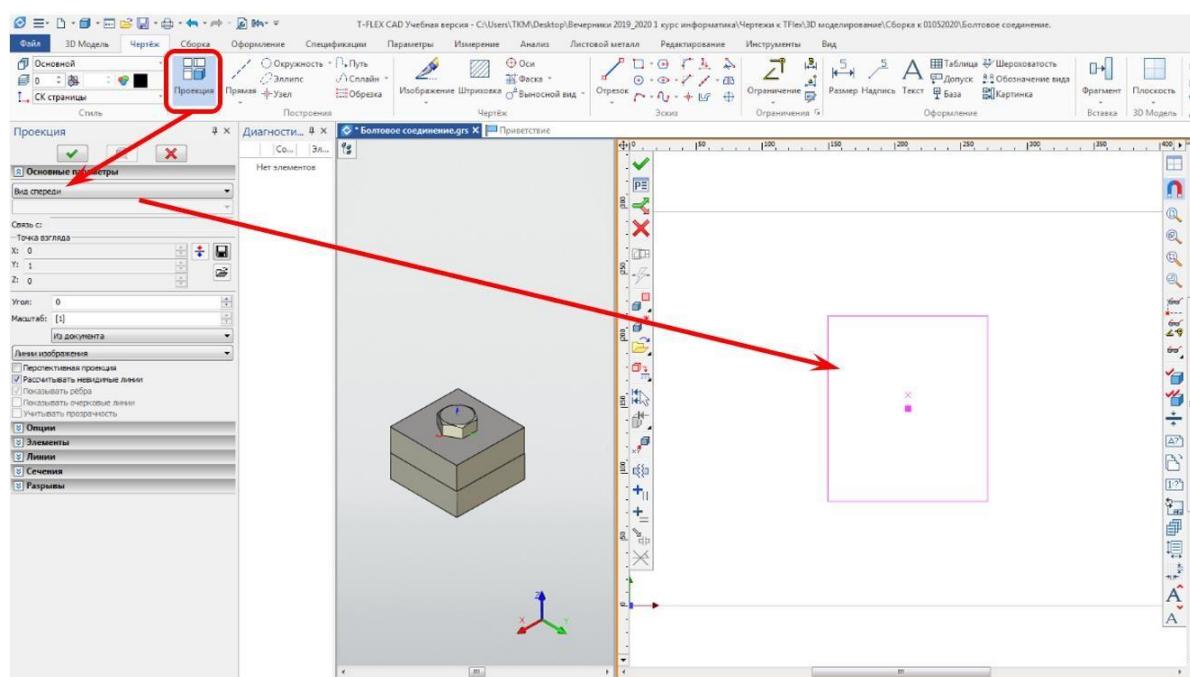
Создание первого вида на чертеже по сборочной 3D модели
